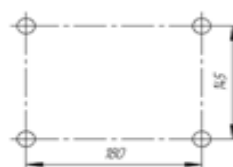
Расположения отверстий для крепления разъединителя
